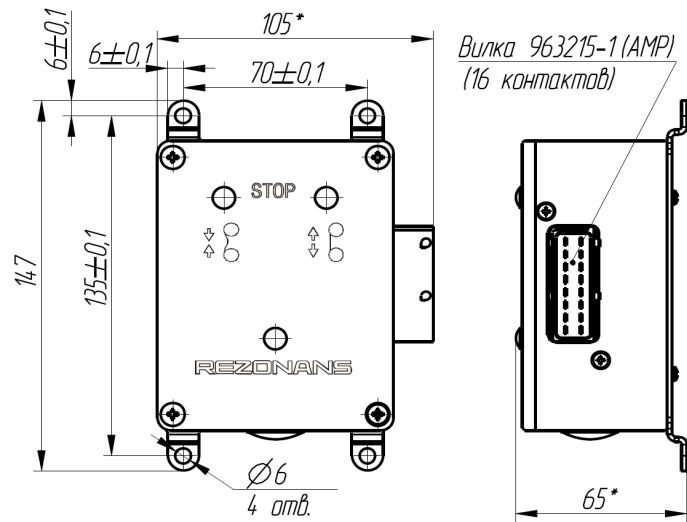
Габаритные и установочные размеры блока управления БУ1-51
